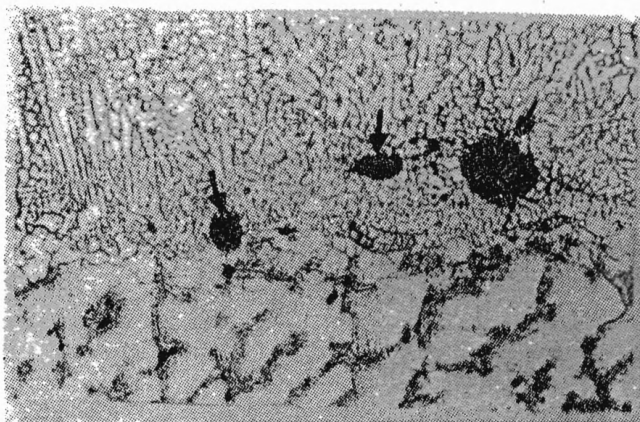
Микропоры при автоматической дуговой сварке стали 45Х25Н20С2 проволокой Св -13Х25Н18 под флюсом АН-26, травление в реактиве № 3 (см. табл. 2), 100<sup>х</sup>
